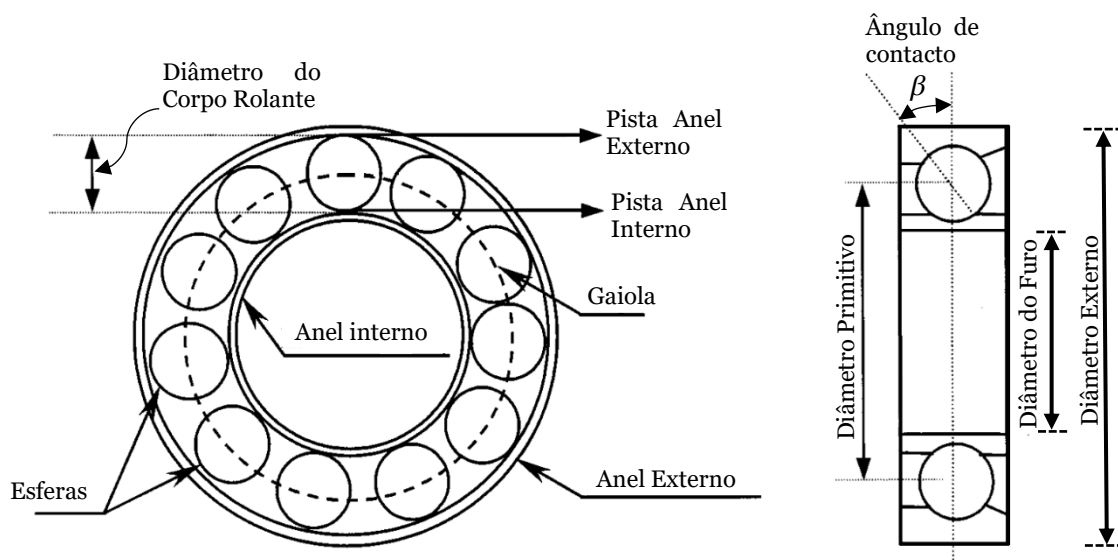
Elementos constituintes e principais dimensões de um rolamento fixo de esferas - adaptado de [26].
